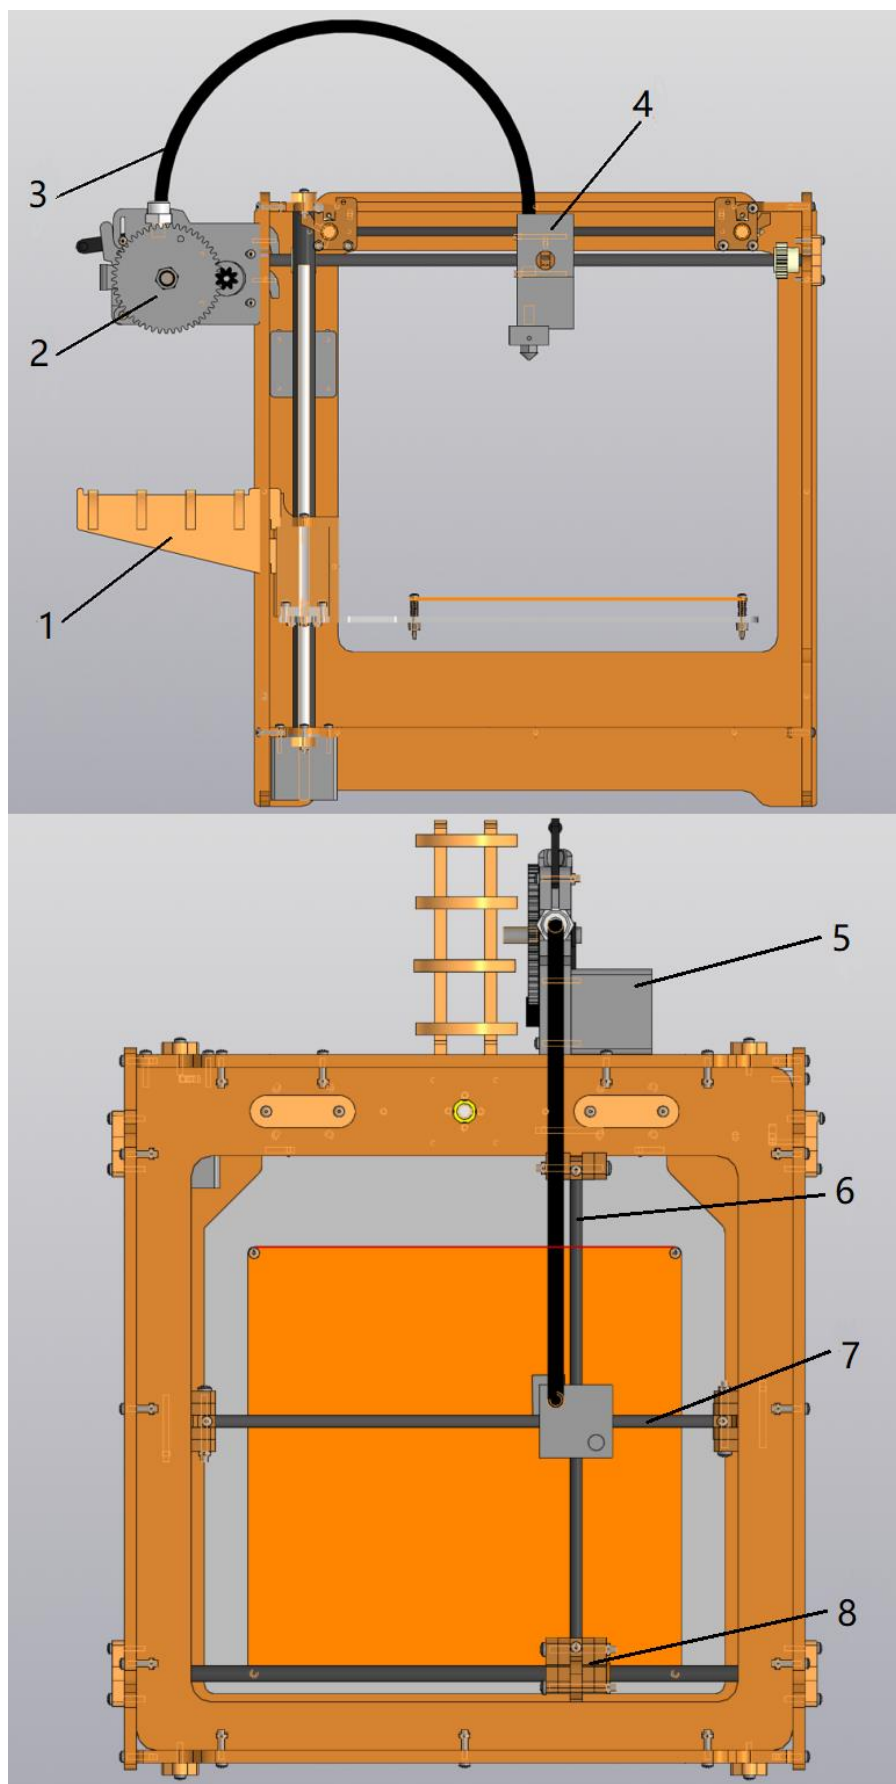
Структура 3D-принтера (1 - опора катушки; 2 - узел подачи; 3 - пластиковая труба; 4 - модуль перемещения; 5 - шаговый мотор; 6 – вал X; 7 – вал Y; 8 – ползушка; 9 – горизонтальный направляющий вал.)
